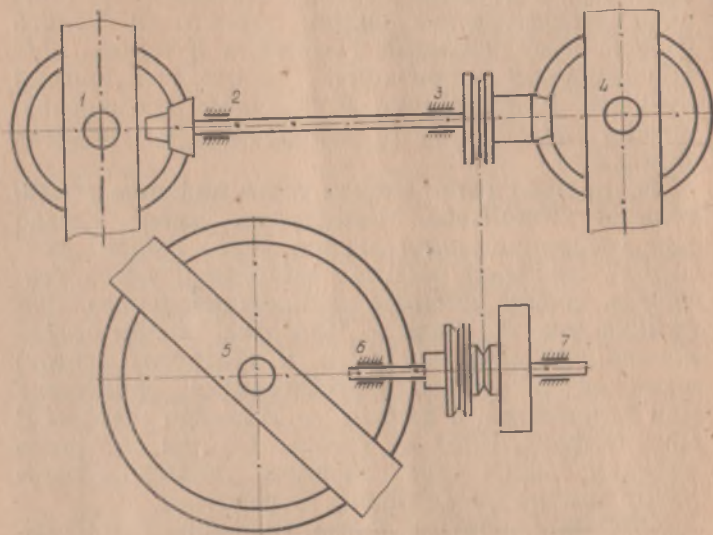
Схема смазки подшипников магнитофона (вид со стороны днища):
